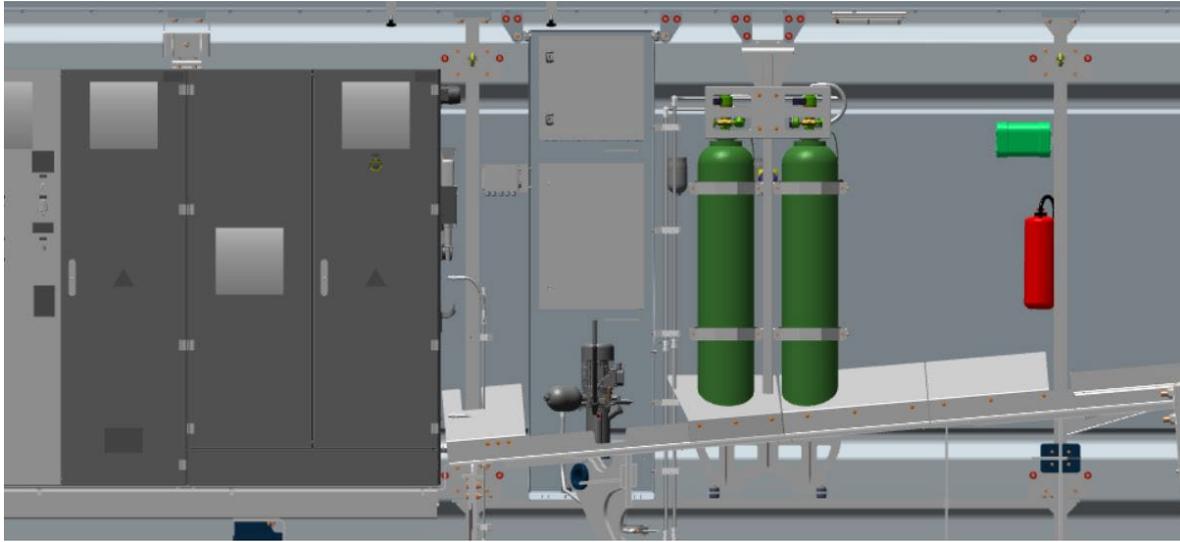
Detailansicht Einbauort Hydraulikaggregat
